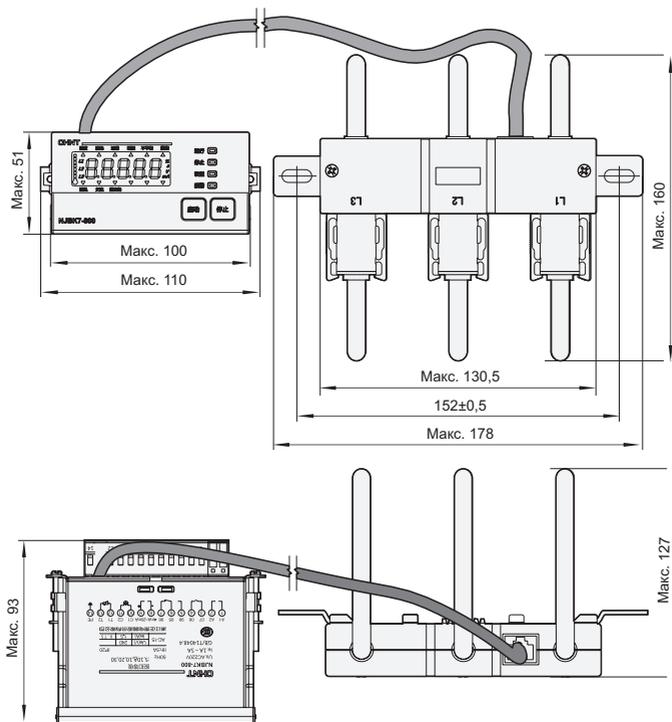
Габаритные и установочные размеры устройства защиты с номинальным током 400, 800 А
